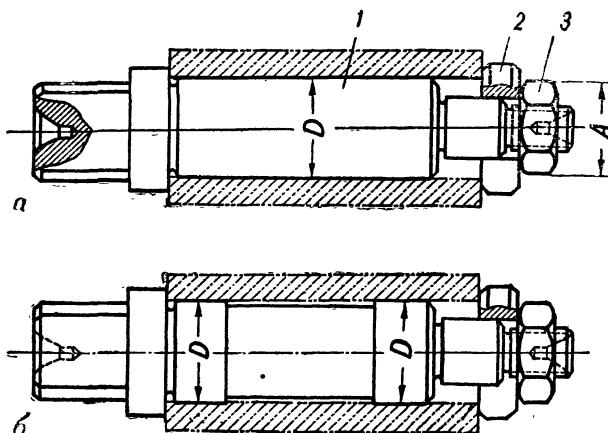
Цилиндрические оправки для свободной установки изделий.
